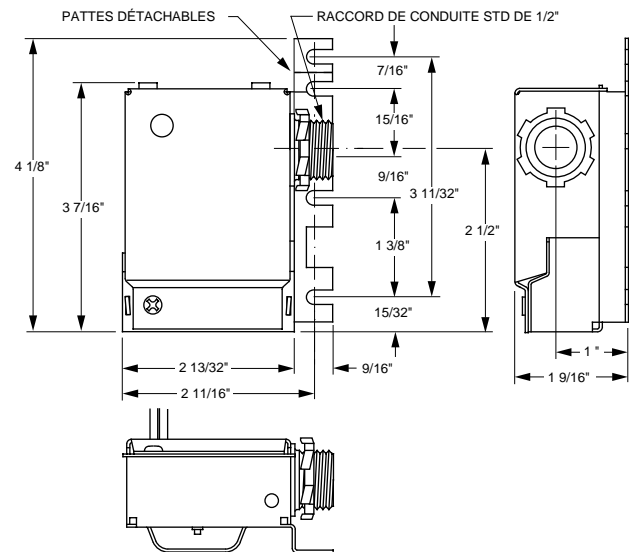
Dimensions de la commande « Level-Temp » de type 24A01/05
